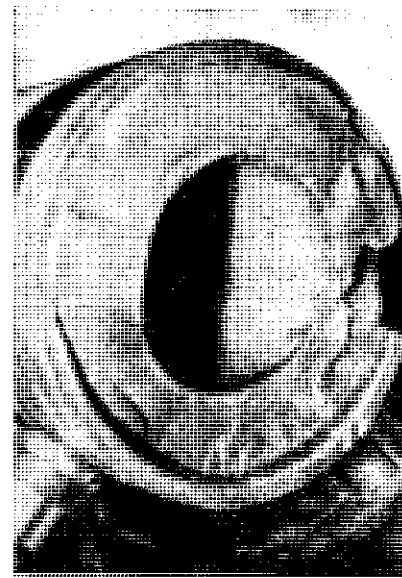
Вид сечения излома гребного вала БМРТ «Дружба» (вал в станке)
